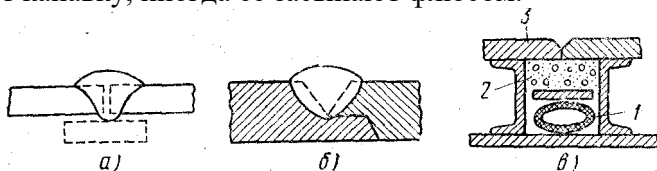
Схема автоматической сварки под флюсом:
